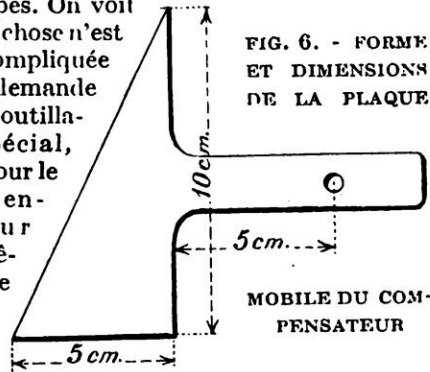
FORME ET DIMENSIONS DE LA PLAQUE
